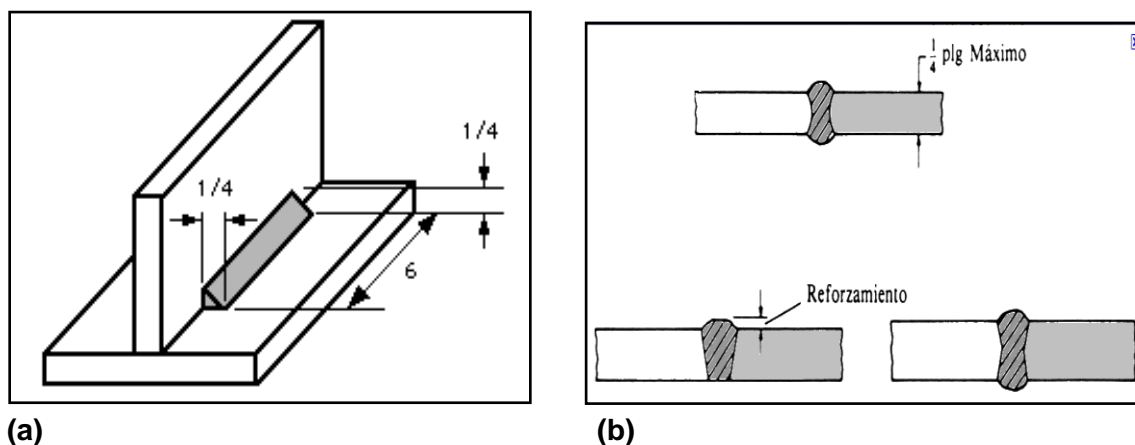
Tipos de soldadura. Fuente: P. T. Houldcroft, Tecnología de los Procesos de Soldadura
